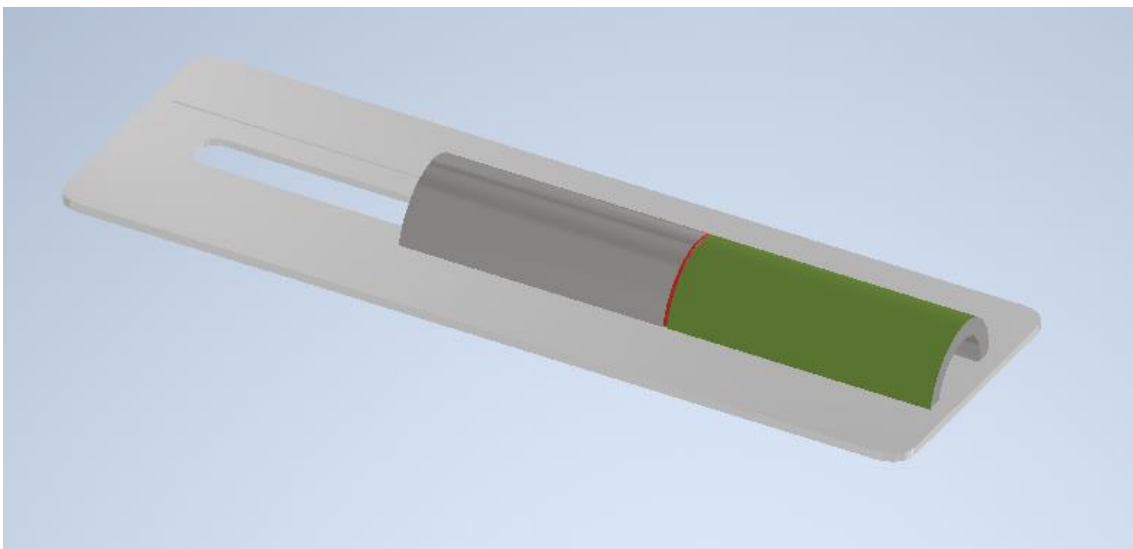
Ejemplo Pieza (Rojo línea de soldadura)
